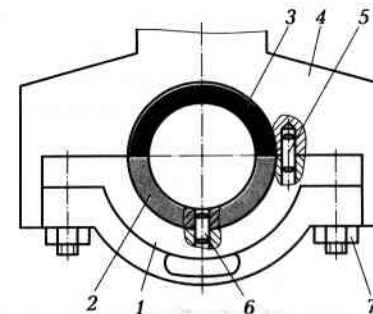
Конструктивная схема подшипника скольжения с разъемным вкладышем:
